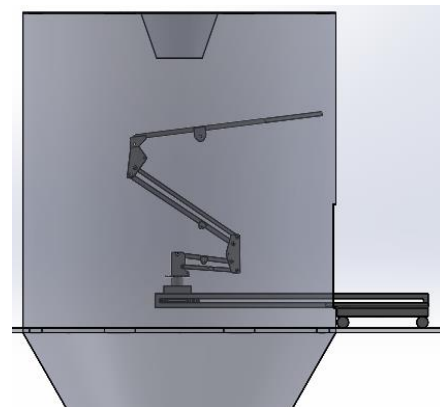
Estructura extensible sobre riel dentro de la cámara de secado.
